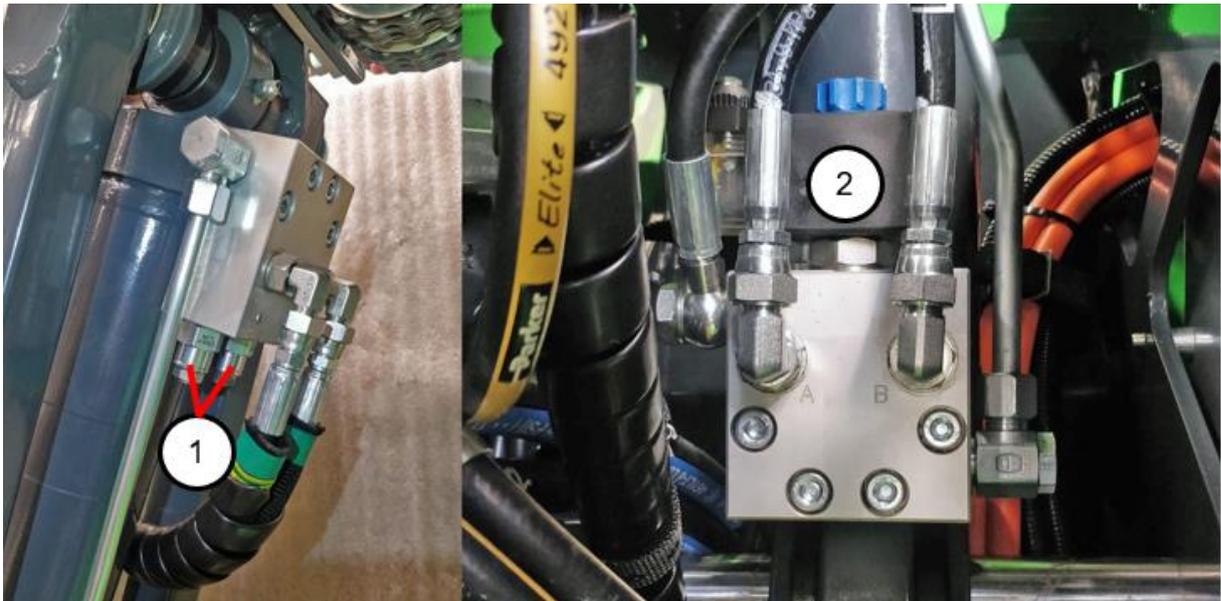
Zylinderhydraulikverteiler. Auslegerarmzylinder (links) und Hubzylinder (rechts).
